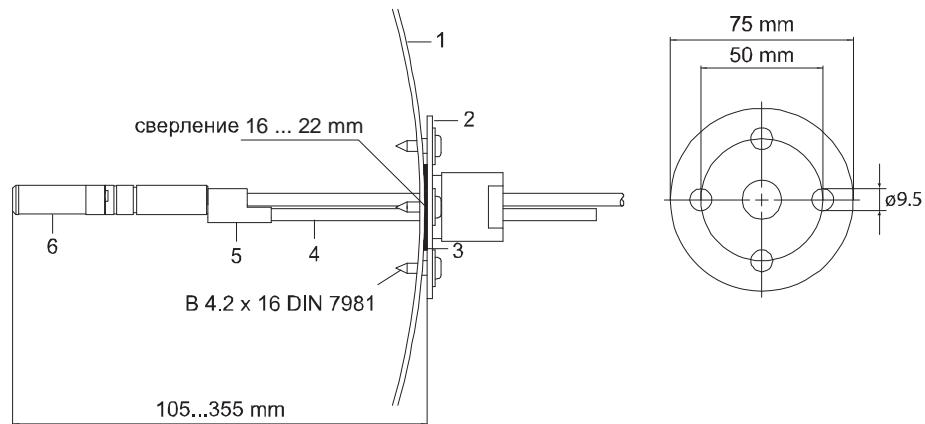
Установка датчика HMP363 в трубопроводе с фланцем и опорной балкой
